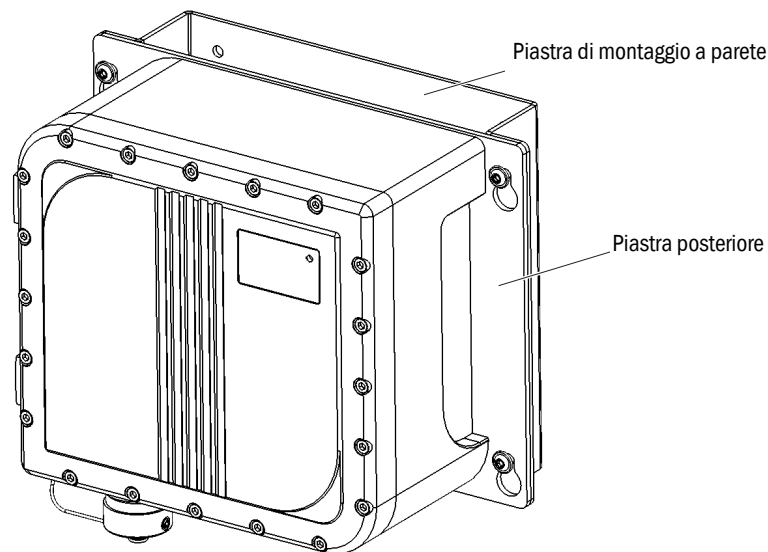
Piastra posteriore e piastra per montaggio a parete opzionale
